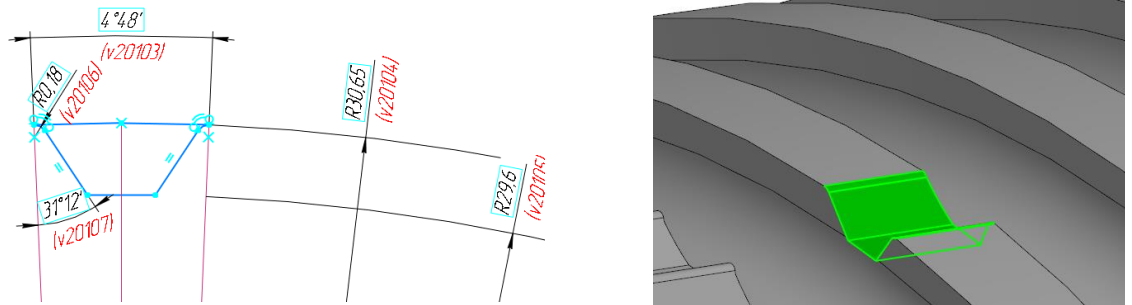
Канавка шліцьового пазу каліброваного зуба
